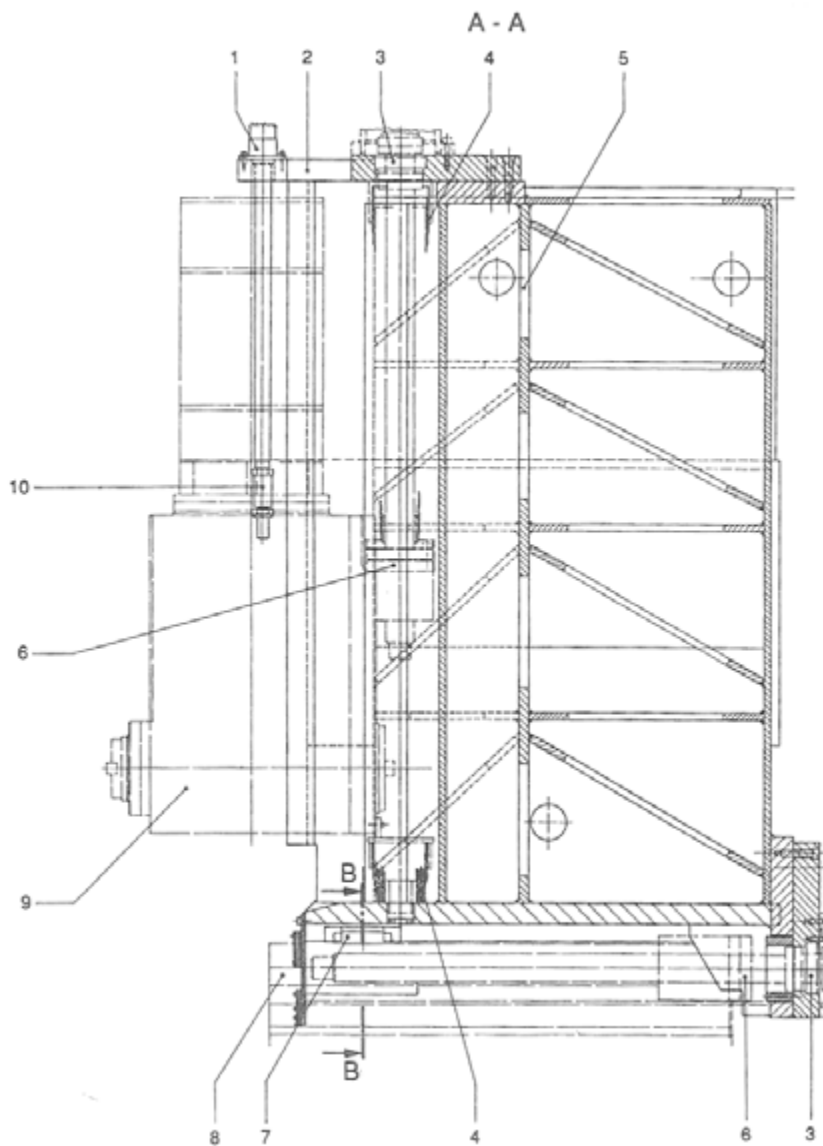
Mechanischer Gewichtsausgleich Einbauskitze
